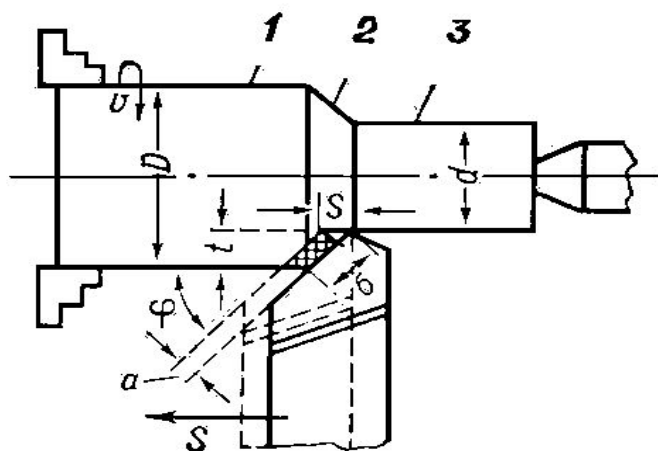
Элементы режима резания при точении: 1 — обрабатываемая поверхность; 2 — поверхность резания; 3 — обработанная поверхность; D — диаметр обрабатываемой заготовки; d — диаметр детали после обработки; a и b — толщина и ширина срезаемого слоя.
